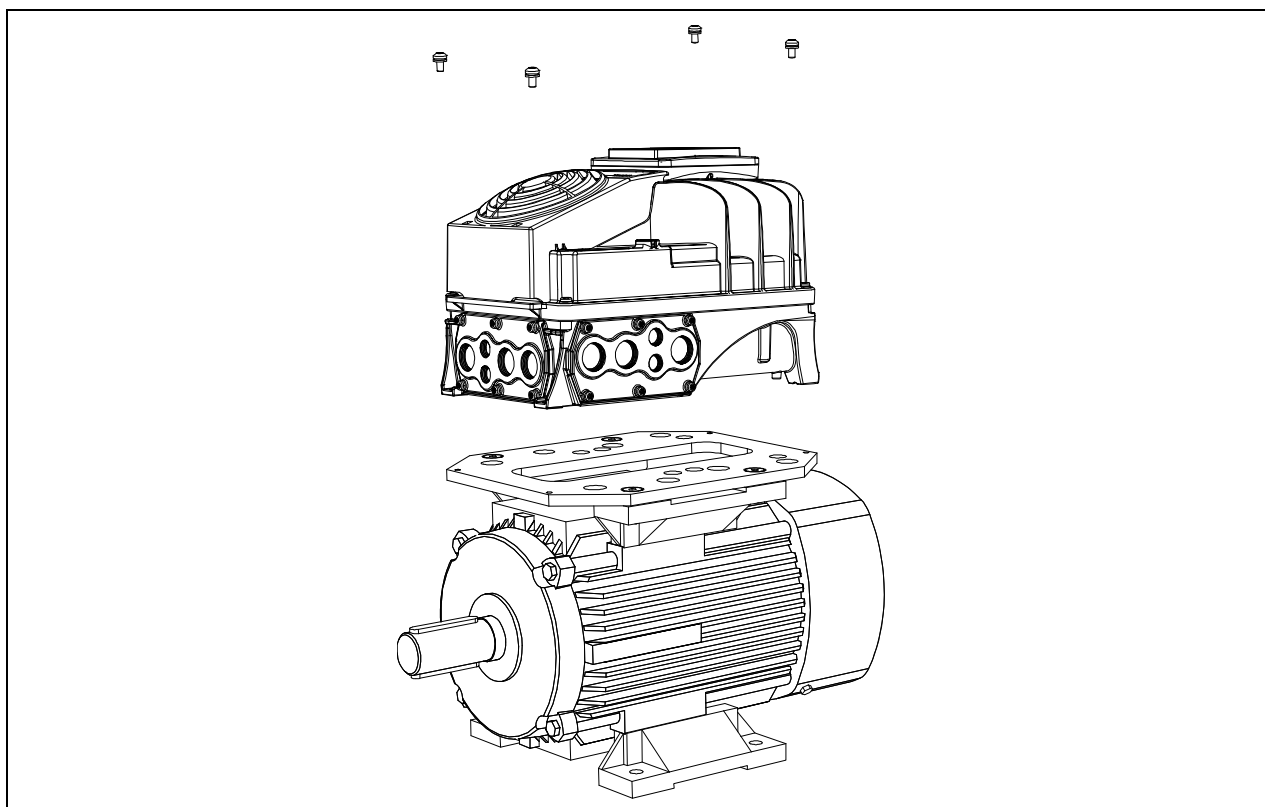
Fissaggio dell'inverter sulla flangia utilizzando 4 viti.
